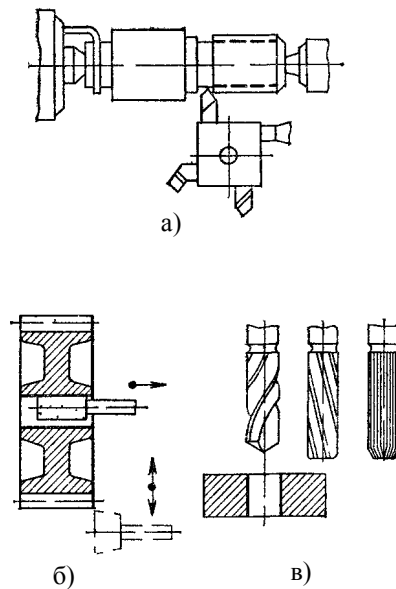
Схеми одномісної послідовної багатоінструментної обробки змінними інструментами:
